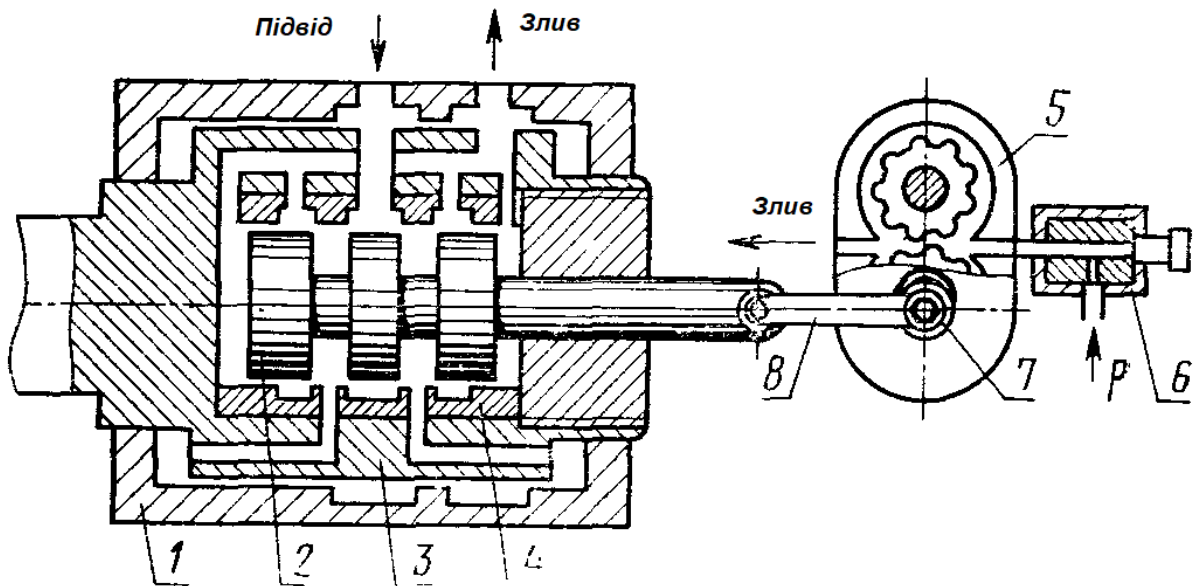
Принципова схема гідромеханічного вібратора
